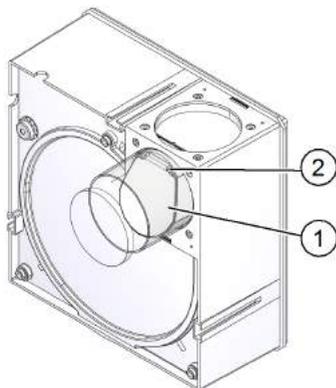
обратный клапан – вытяжка назад, слева сверху
